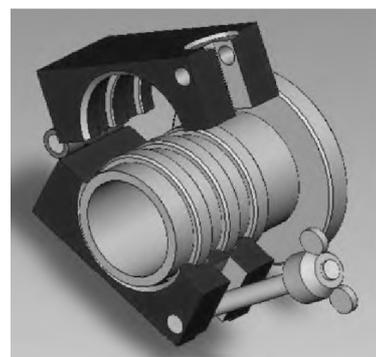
Крепёжное устройство для зажима каркаса напорного рукава, крепёжное устройство для зажима каркаса напорного рукава на втулке соединительной головки
